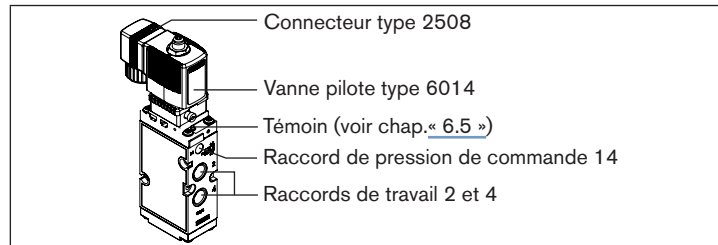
Ensemble de vanne type 6518 /6519 (exemple, type 6519)
